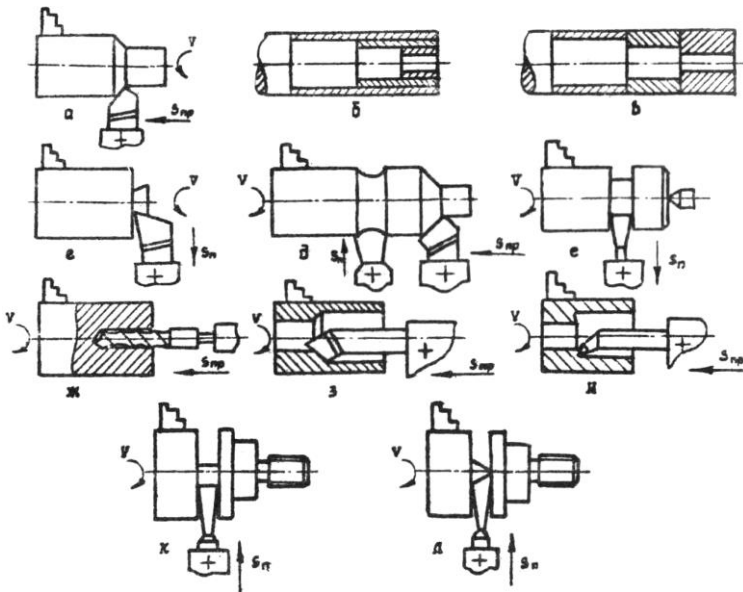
Схемы обработки заготовок на токарно-винторезном станке
